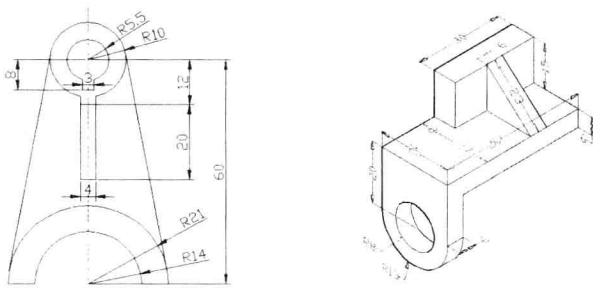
使用 AutoCAD 标注的平面图形和三维图形
